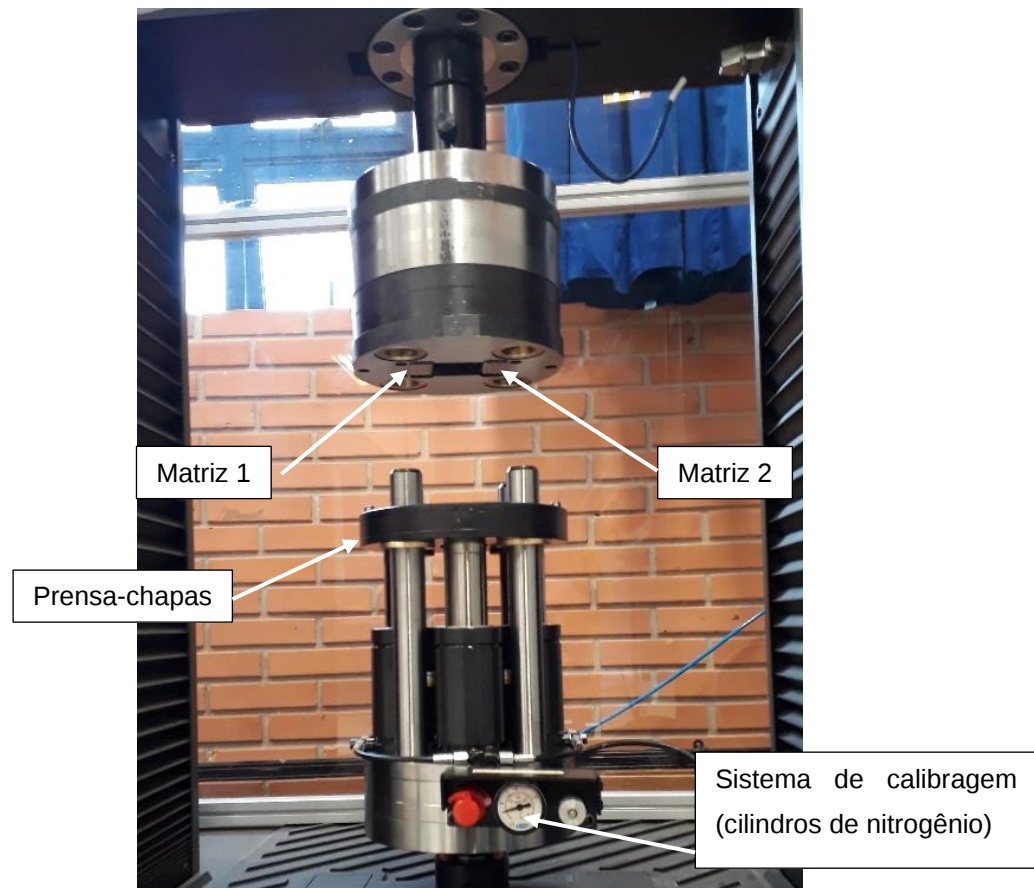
Dispositivo de estampagem instalado na máquina de tração/compressão universal MTS® 100KN
